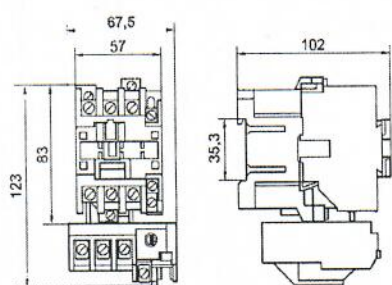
Пускатель нереверсивный ПМ12-025 25А.
